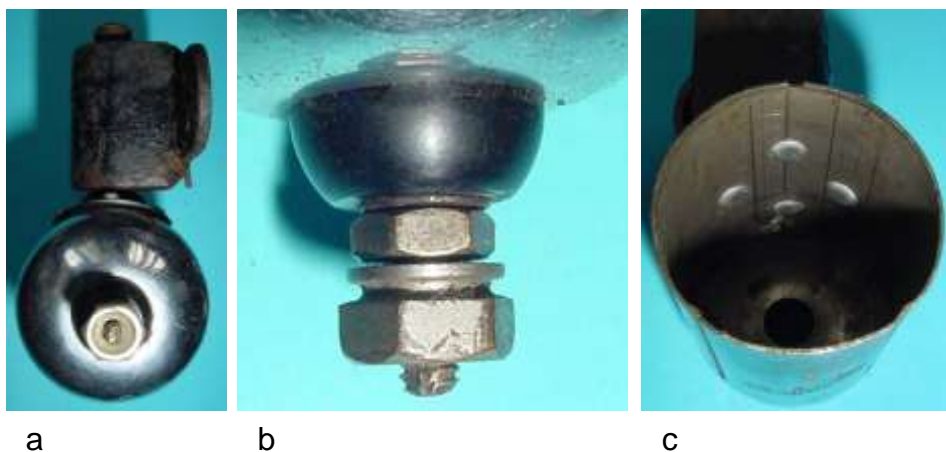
Befestigung des Gehäusetopfes am Kabelanschlussbolzen: a) Boden mit Kippvorrichtung, b) Kabelanschlussbolzen mit Gummiabdichtung, c) Befestigung der Kippvorrichtung am Gehäusemantel
